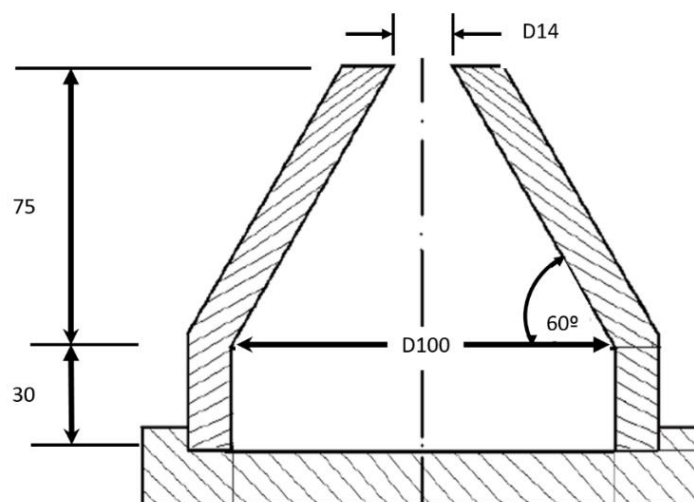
Desenho técnico do molde *Tatur* {adaptado de [2, 27]}.
